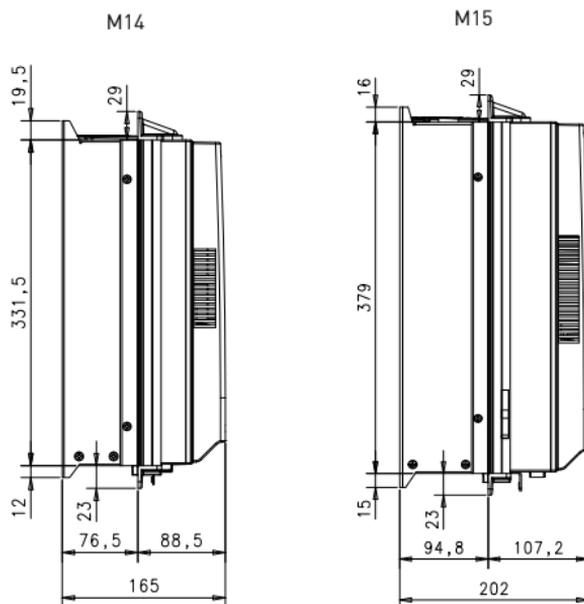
Spessori montaggio a flangia M14 e M15 (Unità: mm)
